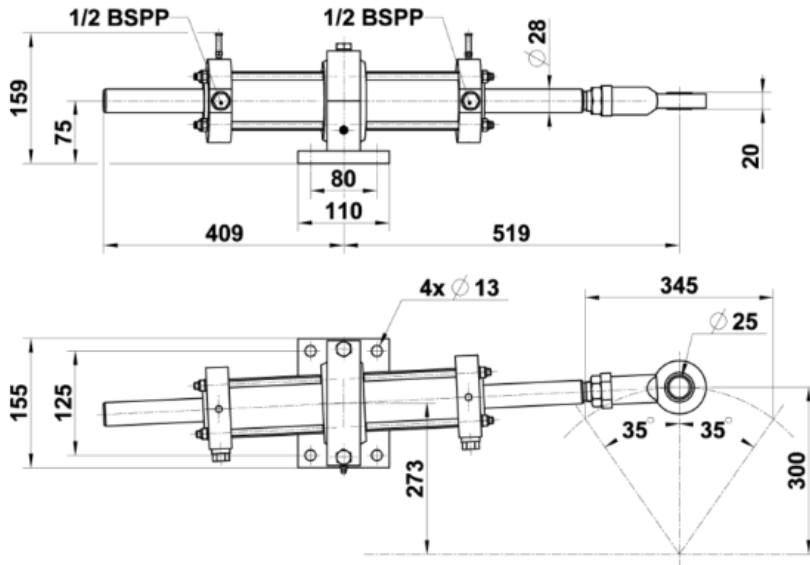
Dimensiones cilindros hidráulicos servomotor. Fuente: Lecomble & Schmitt
